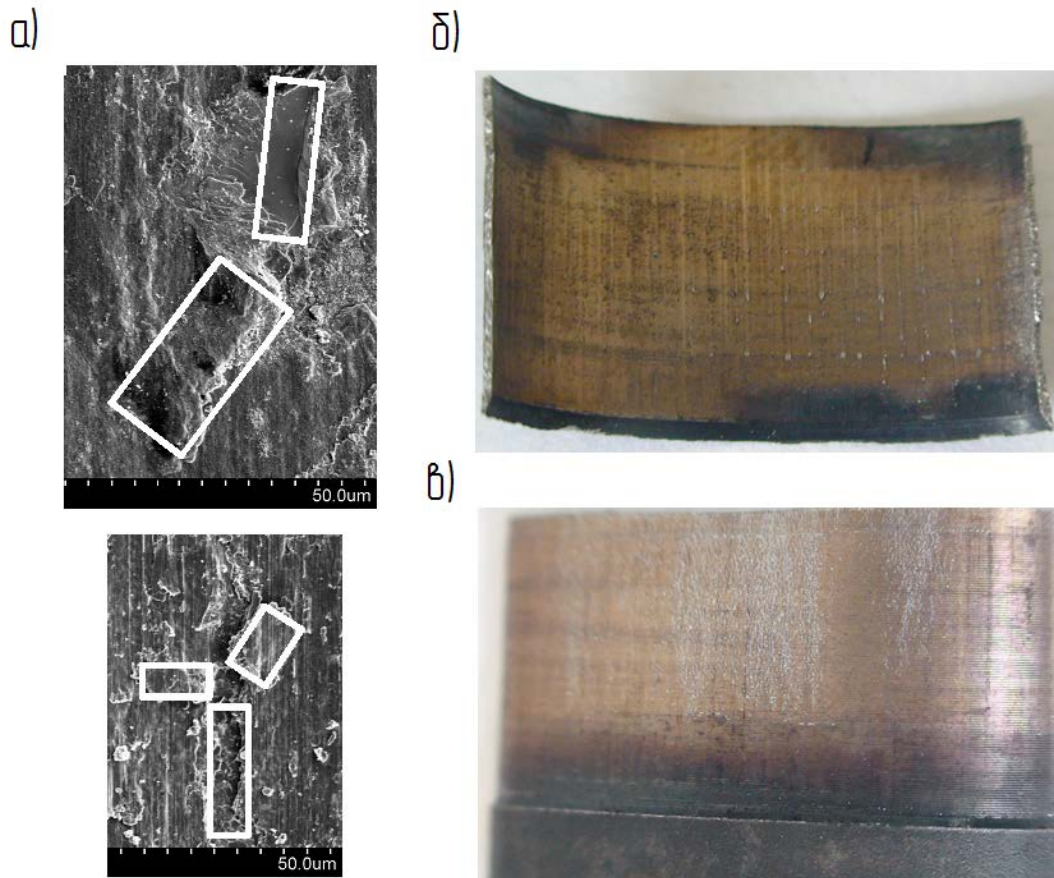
Внутренняя поверхность прессового соединения (натяг 100 мкм) титанового образца после диффузионного спекания на оптимальных режимах: а – участки схватывания; б – внутренняя поверхность прессового соединения охватывающей заготовки; в – внутренняя поверхность прессового соединения охватываемой заготовки
